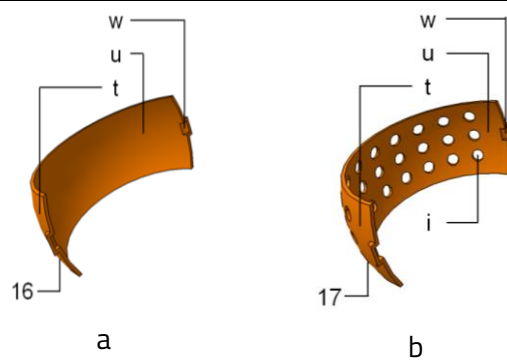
Element de placare, în vedere axonometrică (a – variantă 5; b – variantă 6)<sup>2</sup>
